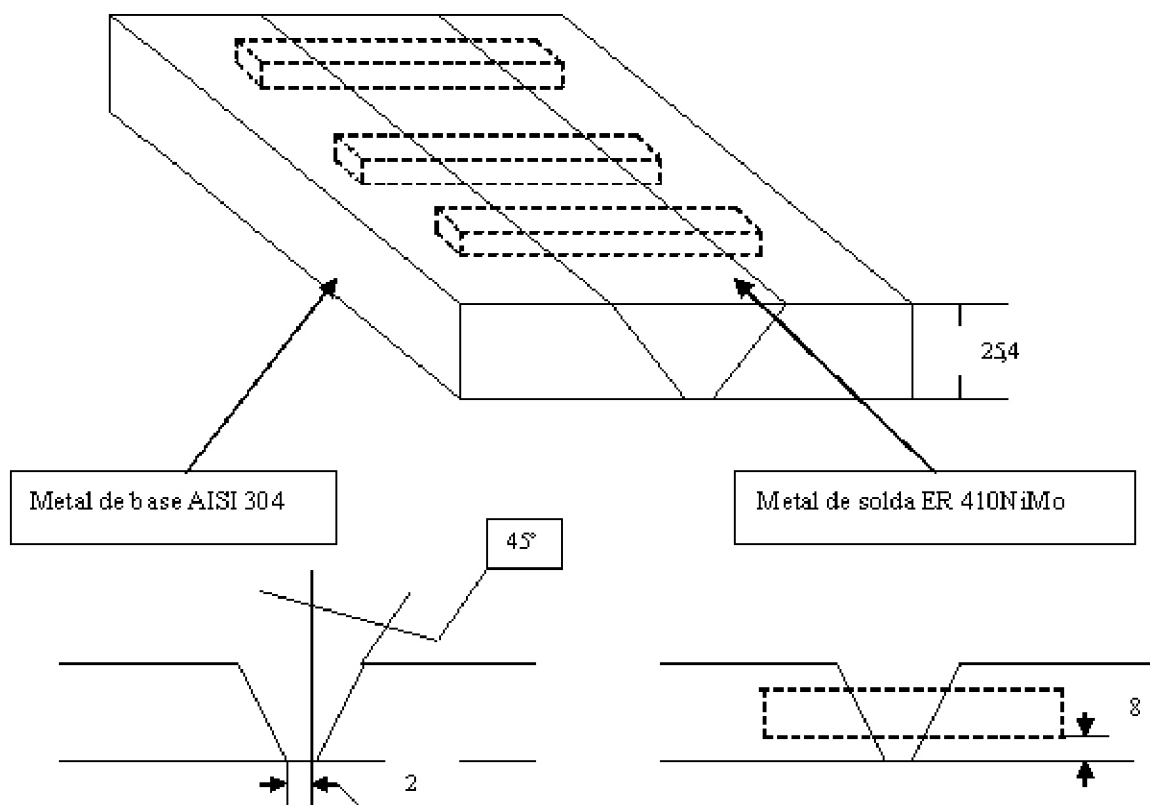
Representação esquemática da junta soldada pelo processo MIG Pulsado, para obtenção de corpo de prova Charpy.
